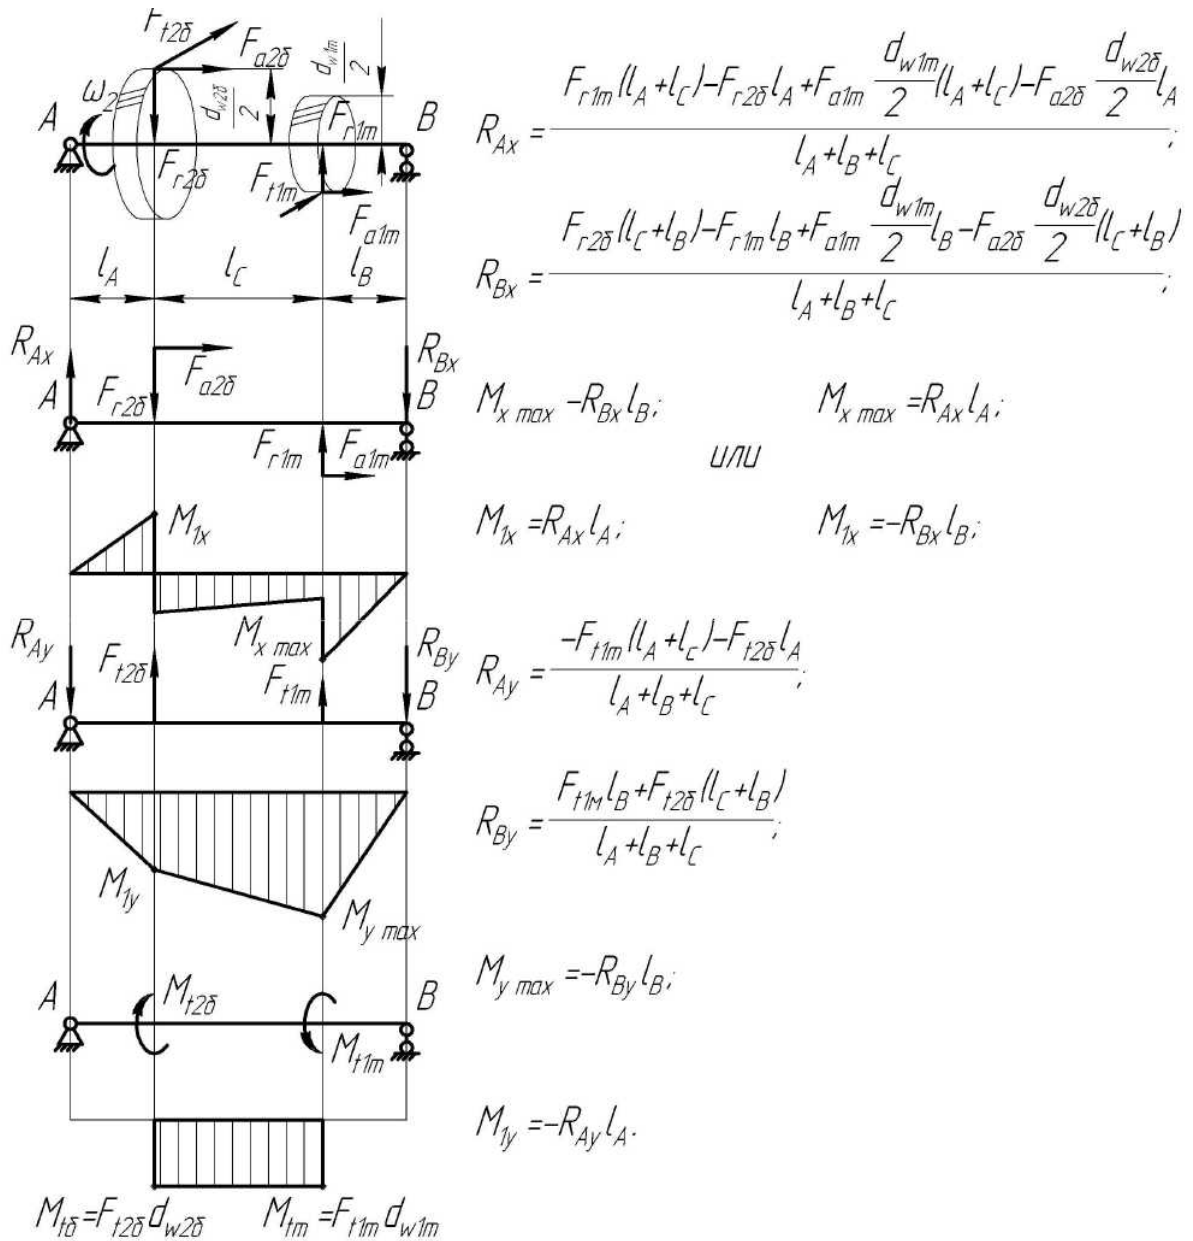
Розрахункова схема проміжного вала циліндричної передачі (при розгляді прямозубого зачеплення не враховувати осьові сили).
